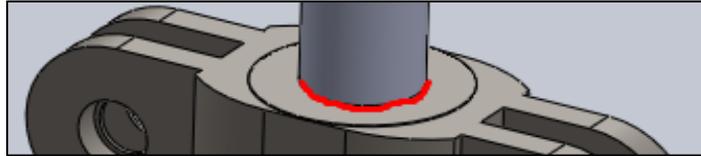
Ubicación del cordón de soldadura entre el tubo central y la placa inferior.
